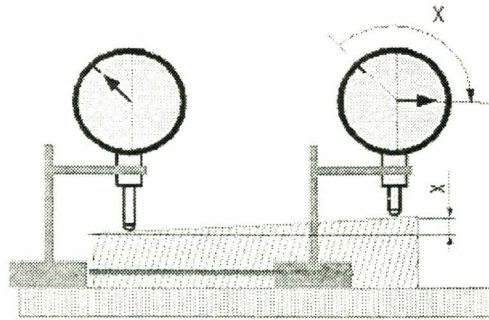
Control de planitud, inclinación. (Mitutoyo).
